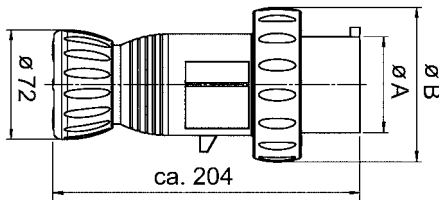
Maßzeichnung Typ 7571/12-506
